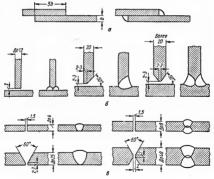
Детели, подготовленные к сварке; а — внахлестку; 6 — в торец; с — в стык.
